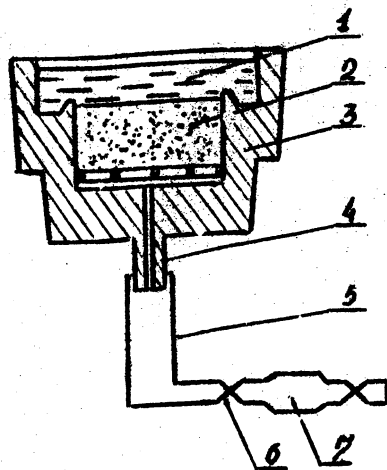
Схема установки для отбора проб формового газа: 1 - жидкий металл; 2 - образец исследуемой смеси; 3 - металлическая полуформа; 4 - штуцер для подсоединения бюретки; 5 - трубка; 6 - зажимы; 7 - бюретка
